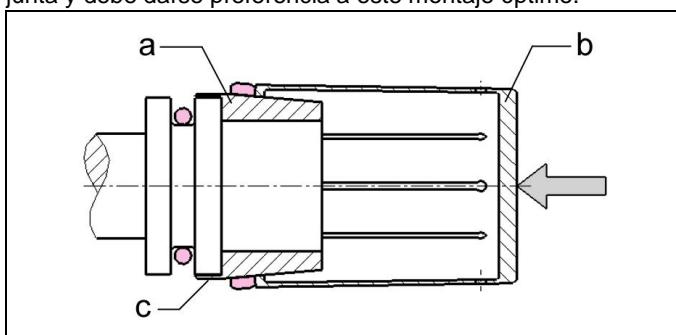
Montaje en una ranura cerrada con casquillo de expansión y de montaje.
